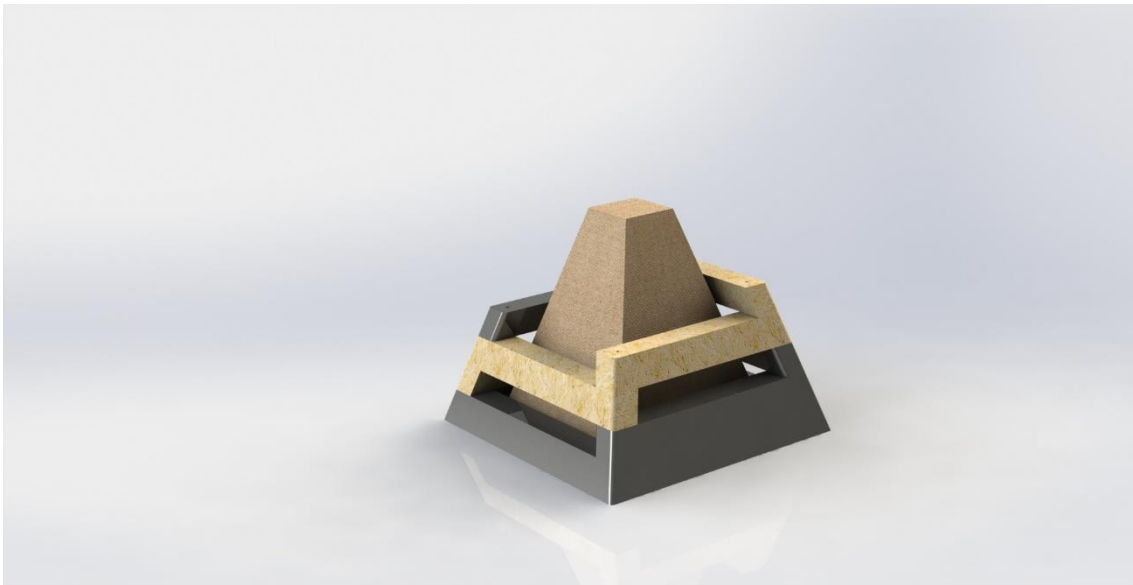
Colocación de las piezas de acero y corcho. Fuente: elaboración propia
